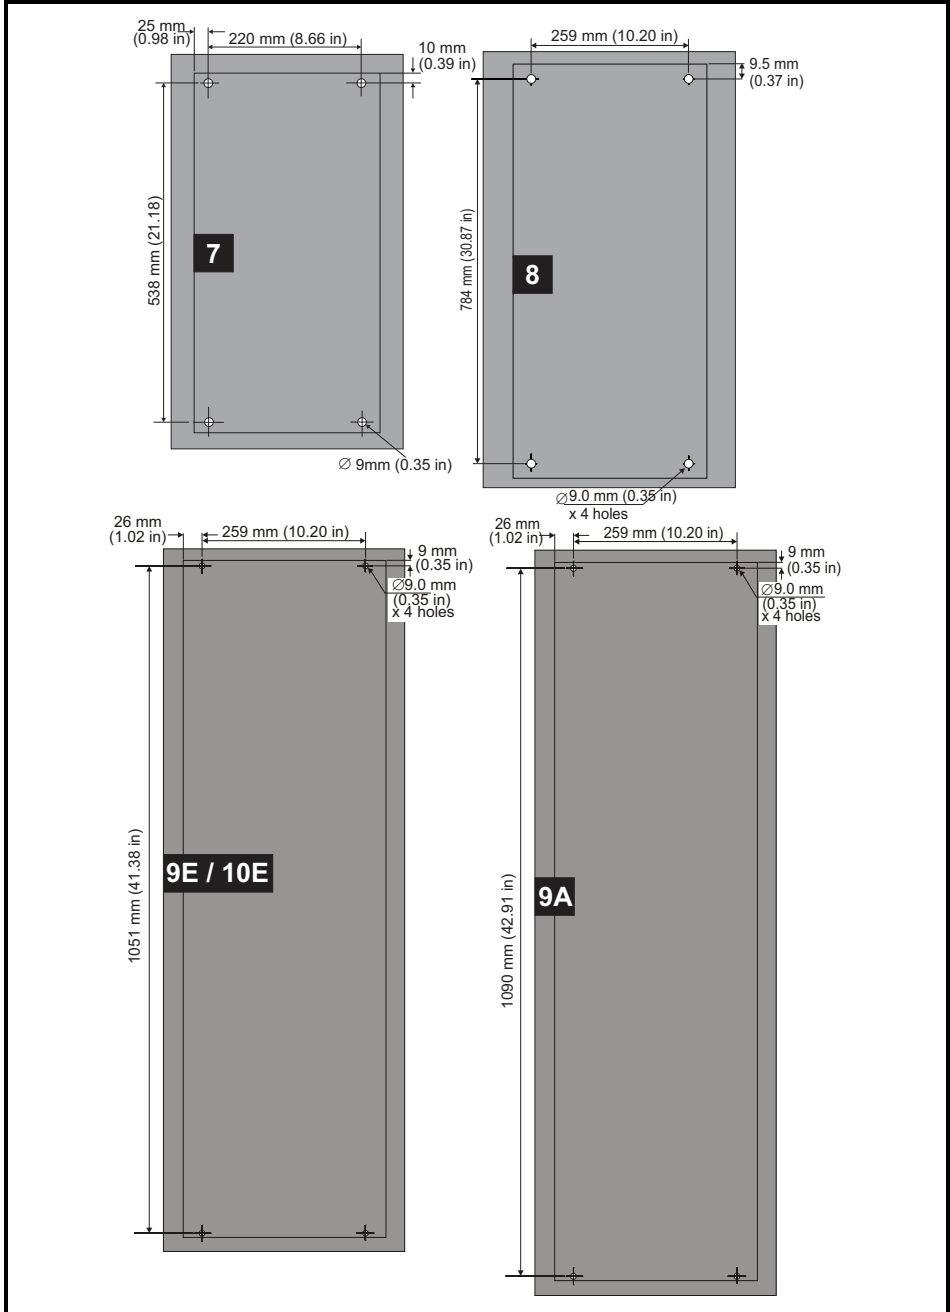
驱动器尺寸（所示为 Unidrive M700 8 型）
